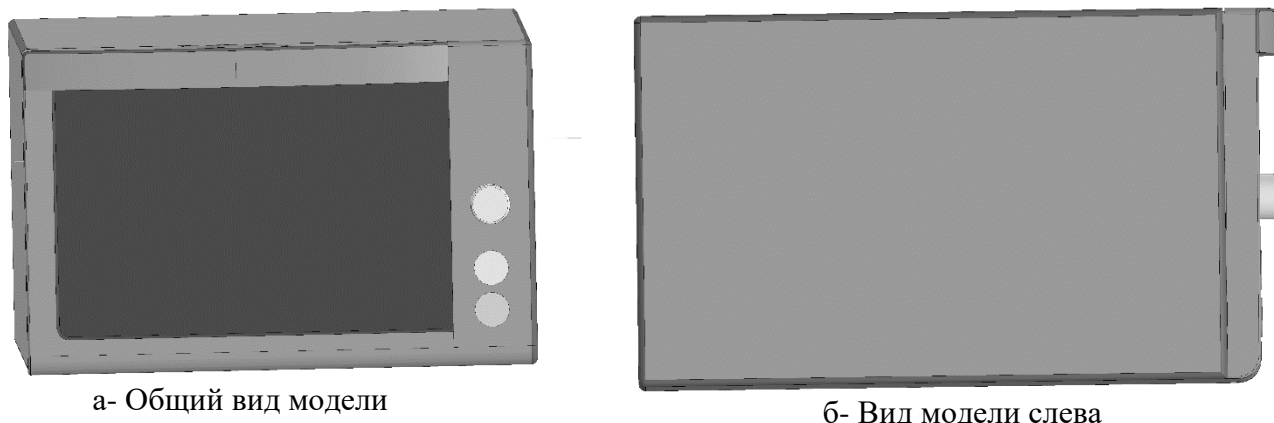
Конструкторская модель СВЧ стерилизатора а- Общий вид модели, б- Вид модели слева
